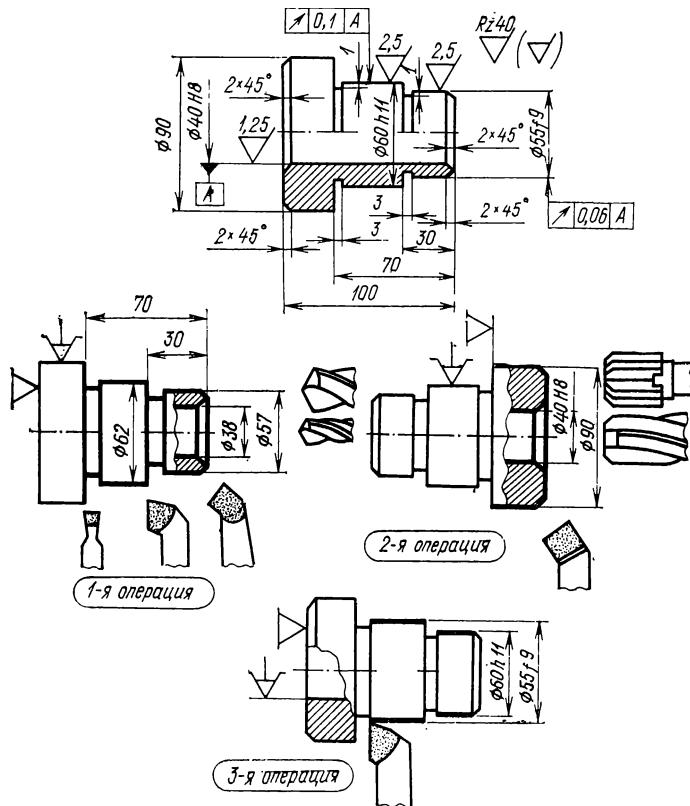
Обработка втулки со ступенчатой наружной поверхностью
